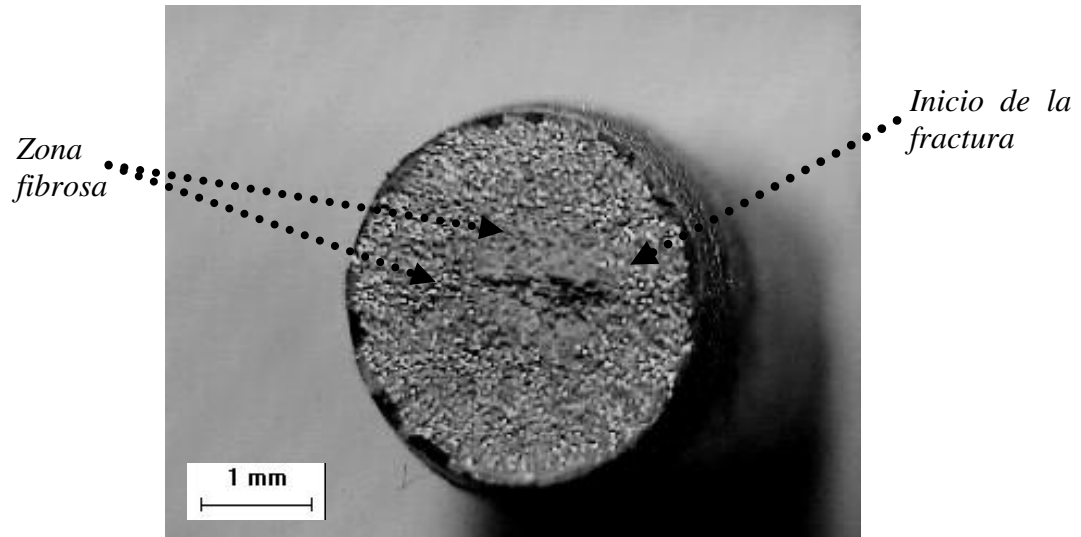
Macrografía de la probeta 1, tipo de fractura frágil
